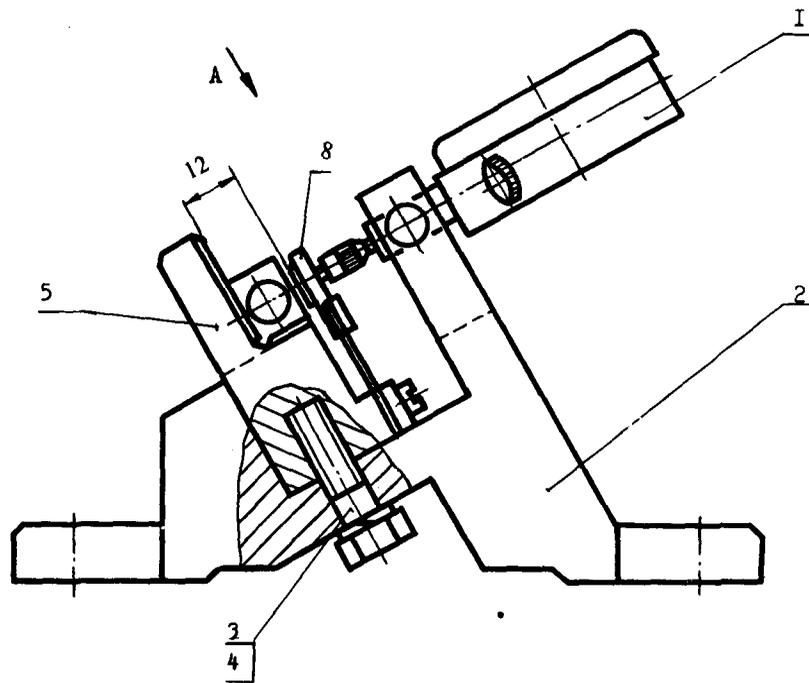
Приспособление для проверки отклонения от цилиндричности гладких валов:
